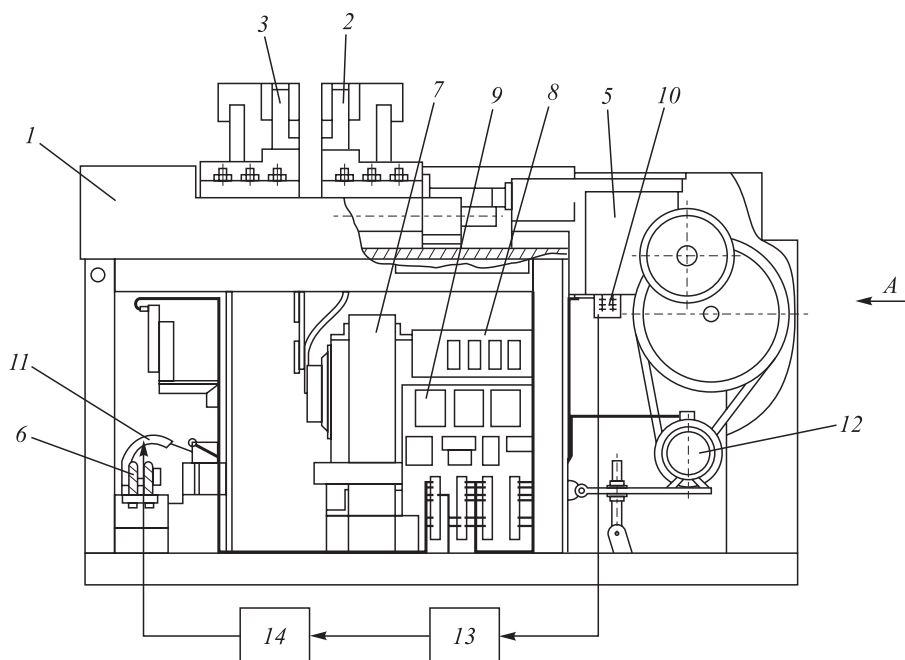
Схема модернизированной машины МС-2008 для контактной стыковой сварки
